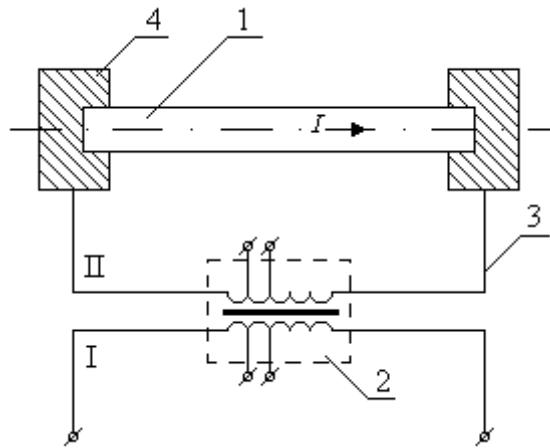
Принципиальная схема электроконтактного нагрева: 1 – заготовка; 2 – нагревательный трансформатор; 3 – проводящие шины; 4 – зажимы (контакты).
